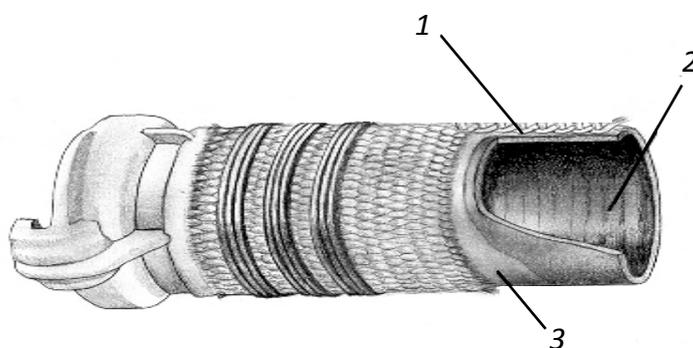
Конструкция напорного рукава с внутренним гидроизоляционным покрытием без наружного защитного покрытия каркаса:
